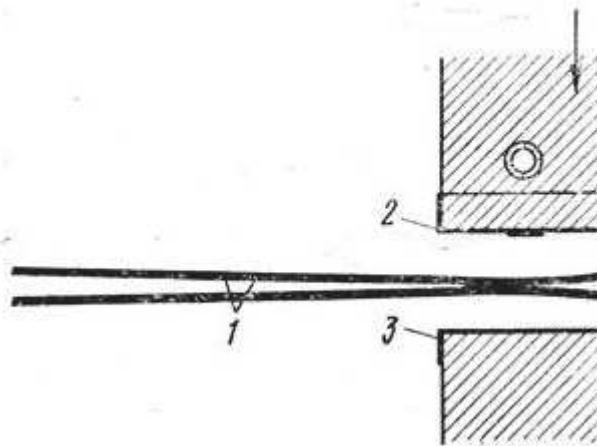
Схема контактено-термічного способу зварювання
